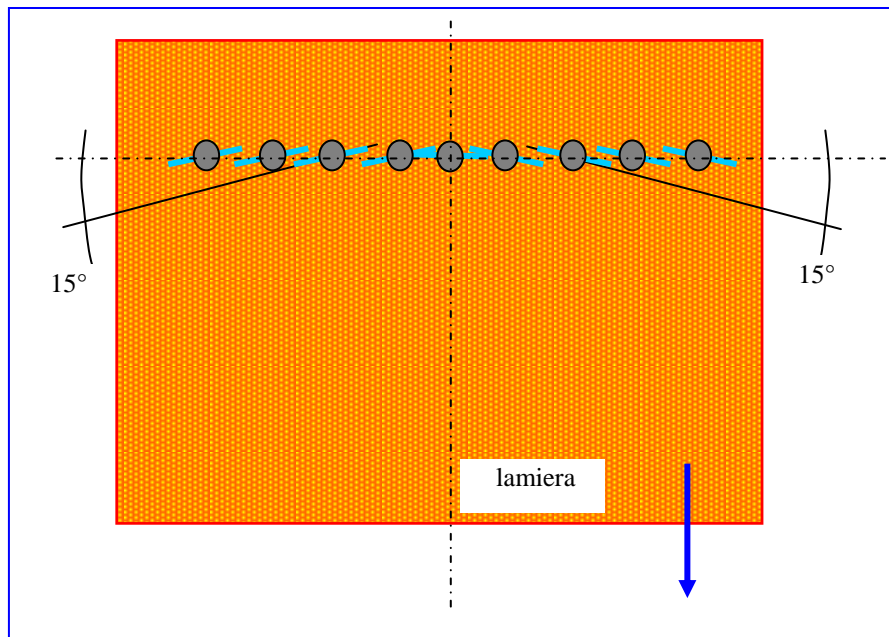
Inclinazione degli ugelli delle due rampe rispetto all'asse trasversale della lamiera
